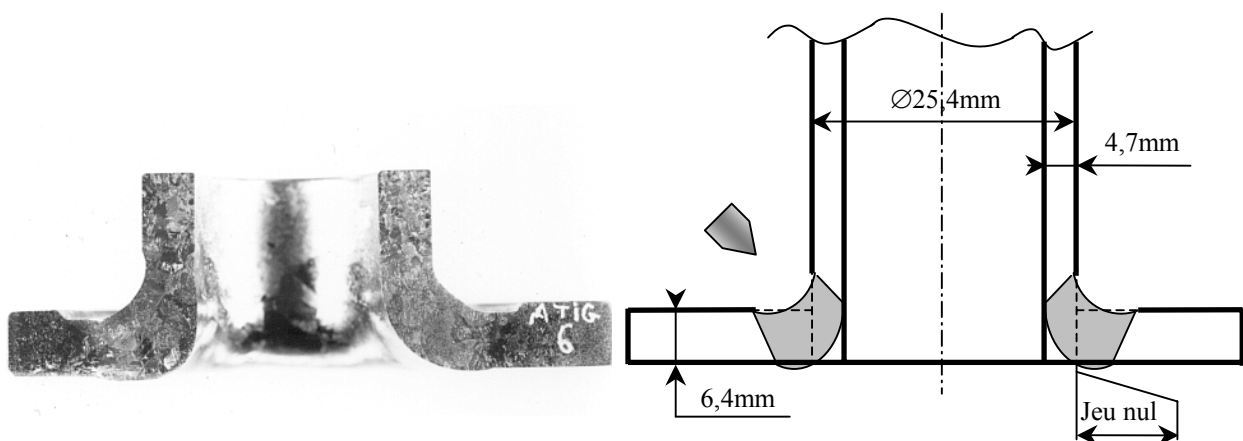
Piquage tube sur plaque, soudure manuelle orbitale ATIG - 130A (T40)
